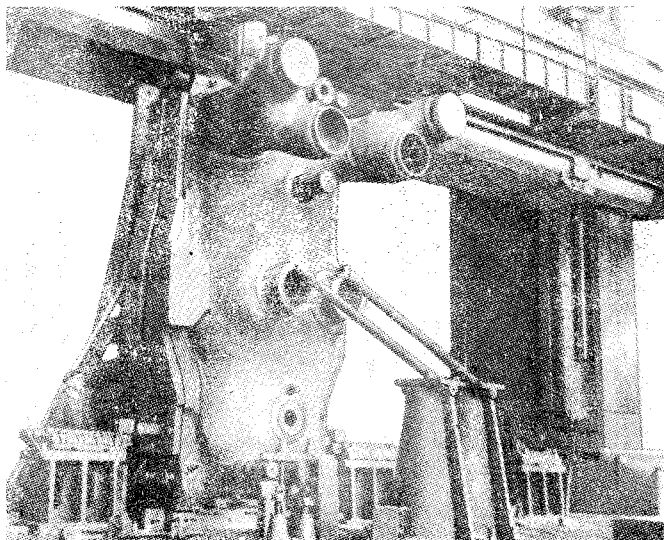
Корпус цилиндра в сборе под обработку на карусельном станке
